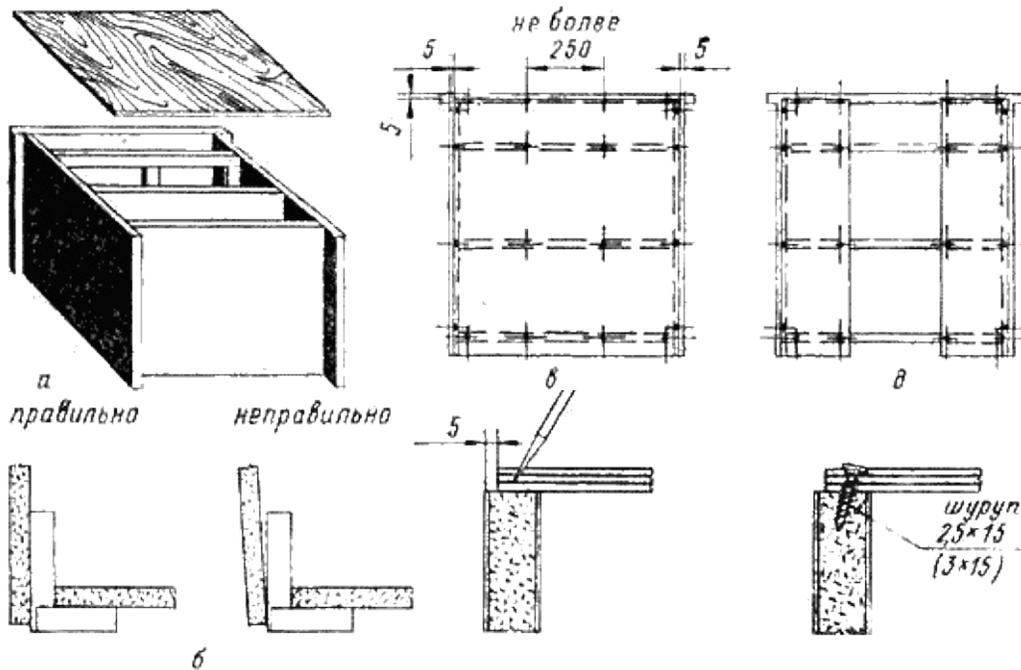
Крепление задней стенки разделочного стола-шкафа: а — примерка задней стенки; б — проверка угла между боковой стенкой и днищем; в — расположение шурупов для крепления задней стенки; г — установка шурупов; д — вариант замены задней стенки связующими полосами
